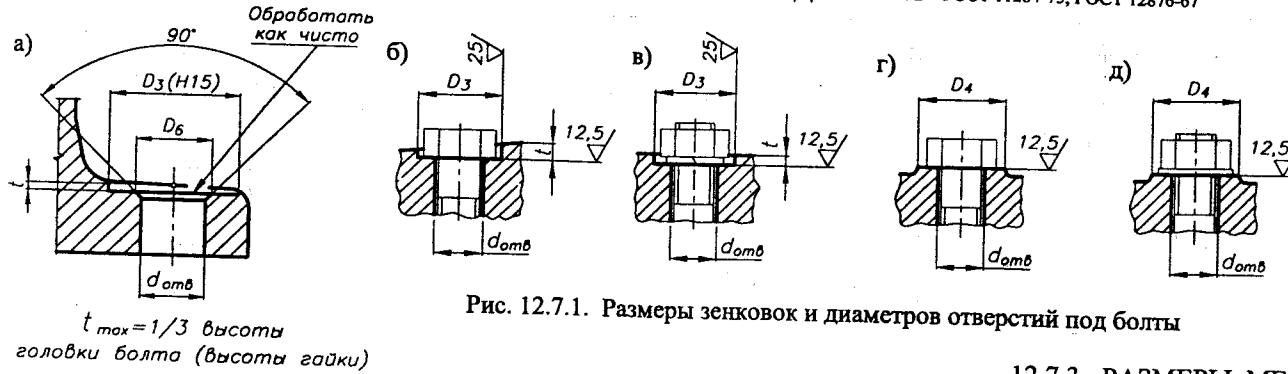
Размеры зенковок и диаметров отверстий под болты
